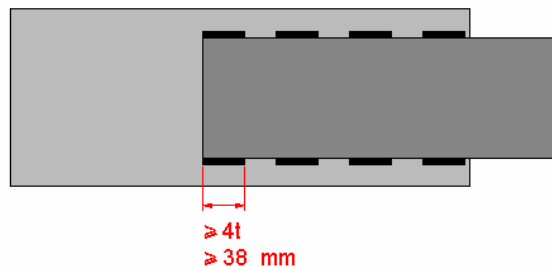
Dimensiones de soldadura tipo filete intermitente
